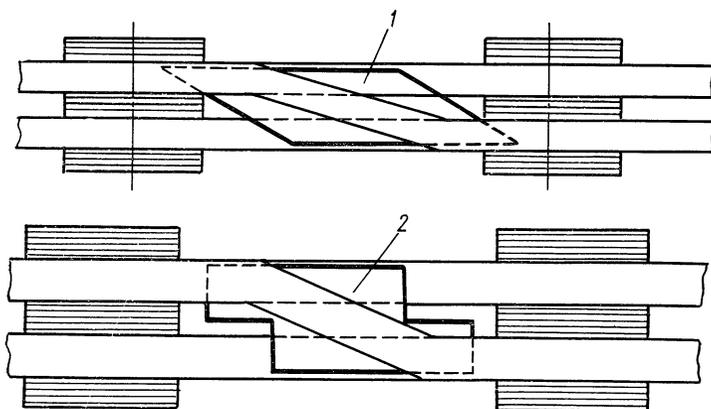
Изоляция переходов — подкладки под наружные переходы:
